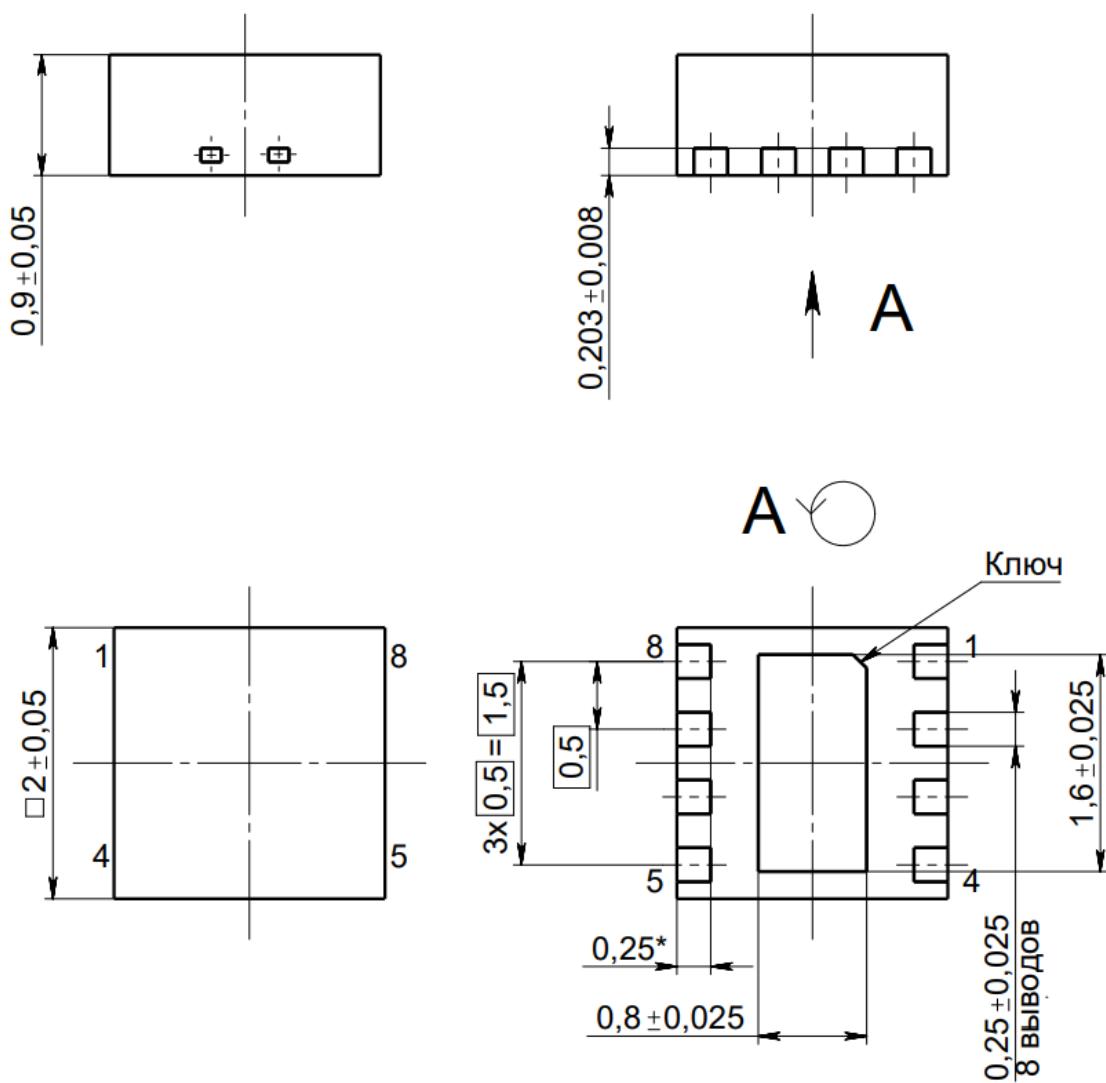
Габаритный чертеж корпуса 5239.8-1 К (размеры в мм)
